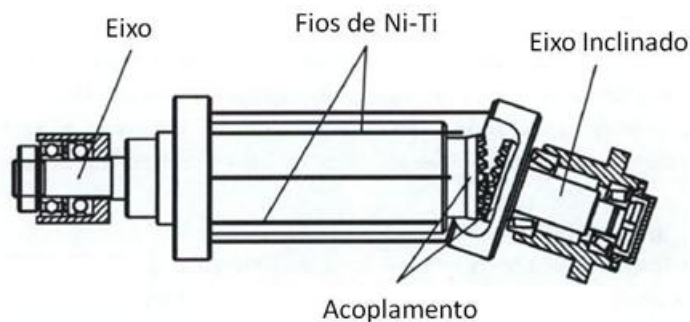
Mecanismo de conversão axial-rotacional de Glasauer (Glasauer, 1996. Modificada).
